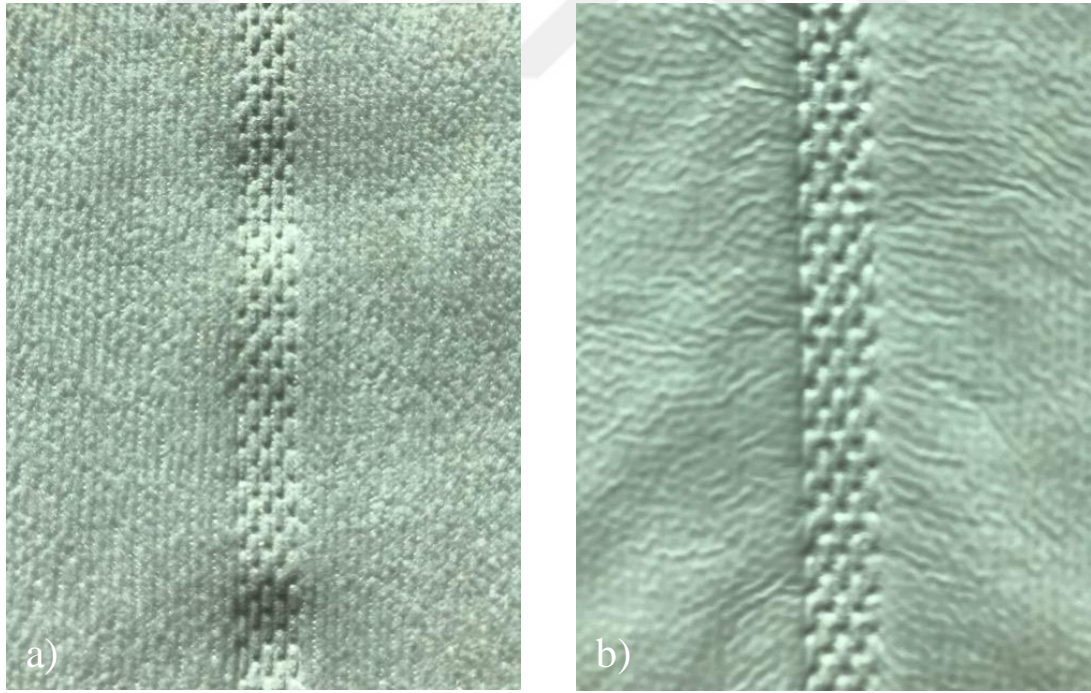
Ultrasonik dikiş makinesinde R2 ile dikilen O2 kumaşının görüntüsü
